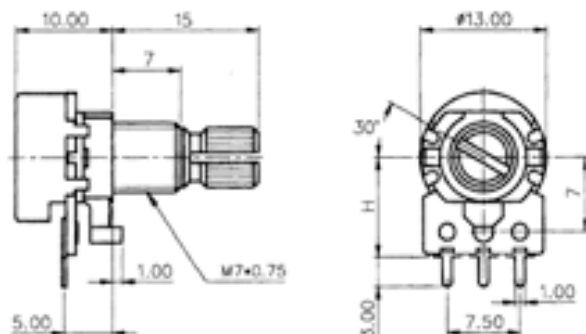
Габаритні розміри змінного резистора 3329Н
